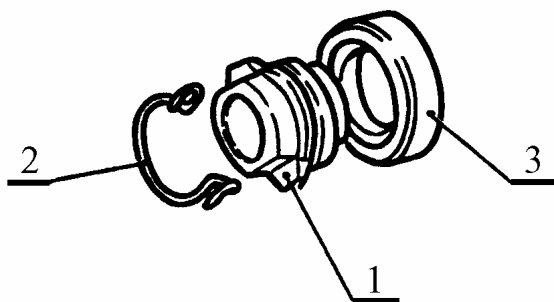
Детали муфты 2101-1601180 подшипника выключения сцепления в сборе:
